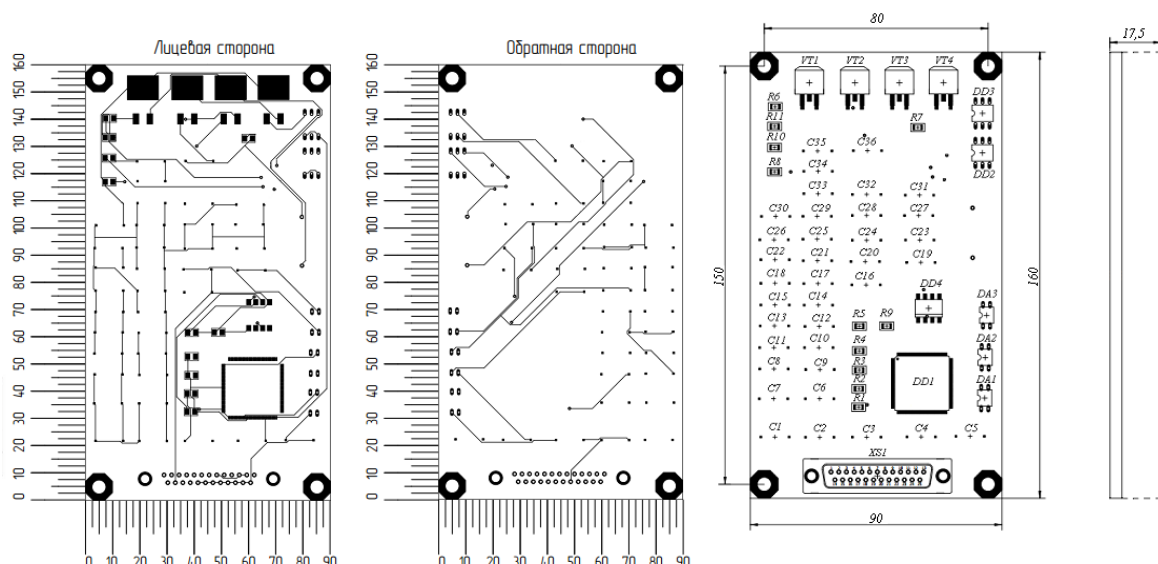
Разработанная двухсторонняя печатная плата и сборочный чертеж устройства
